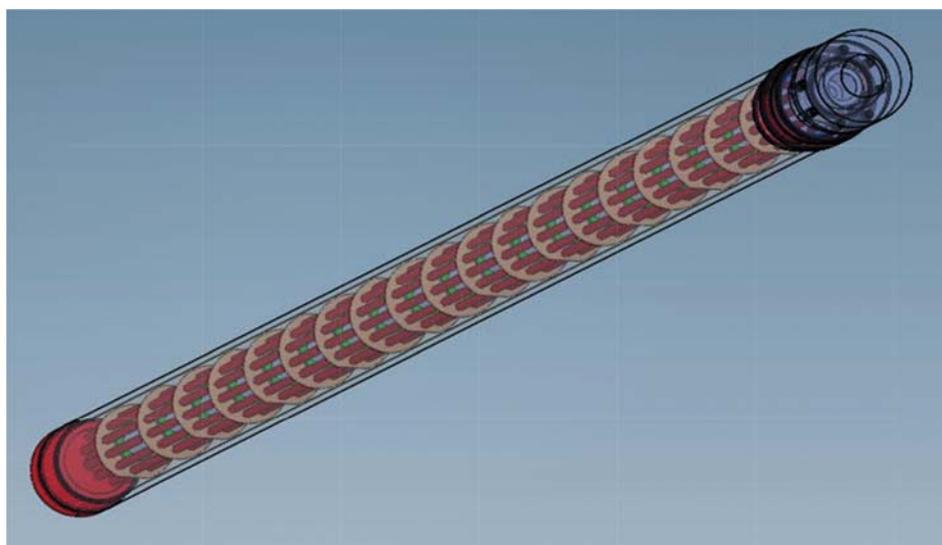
Внешний вид забойного проточного нагревателя ЗПН.
